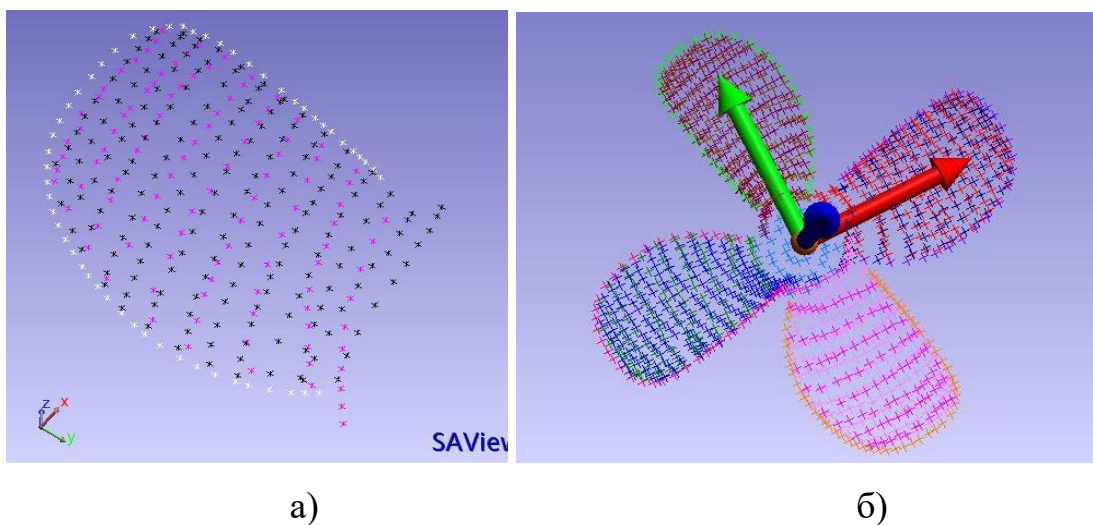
Вихідна 3D-модель заготовки 4х-лопастевого ГВ: а) координати кромки і лопасті; б) 3D-модель заготовки
